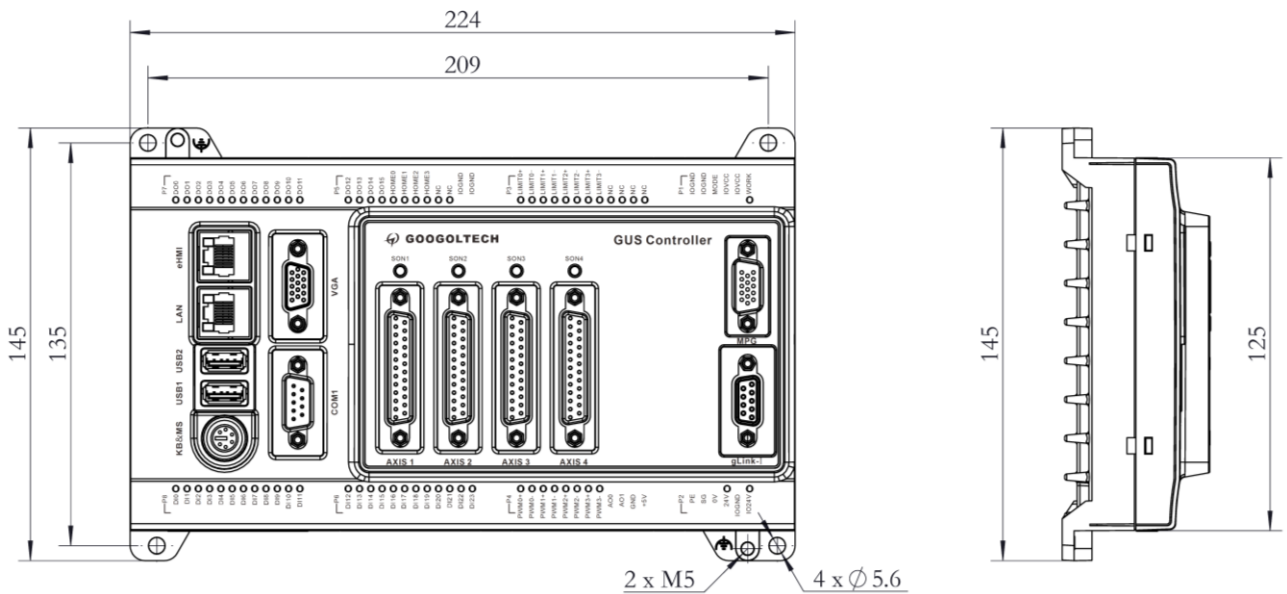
GUS-400-TG02-XXXX 控制器尺寸图
